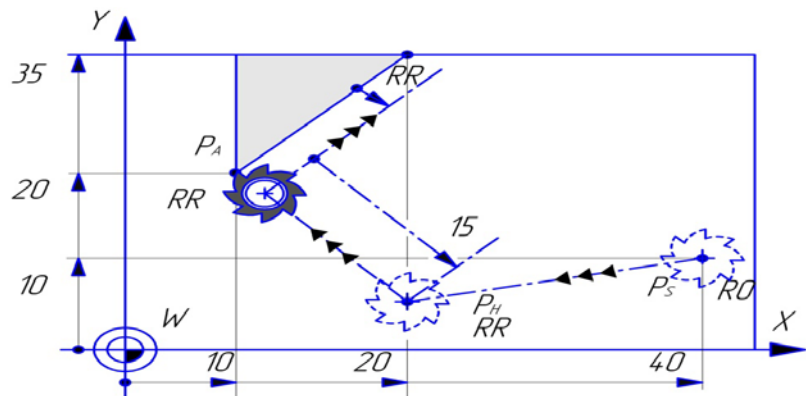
Подвод инструмента перпендикулярно обрабатываемому контуру
